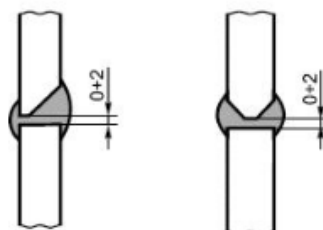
Виды горизонтальных сварных соединений стенки.
